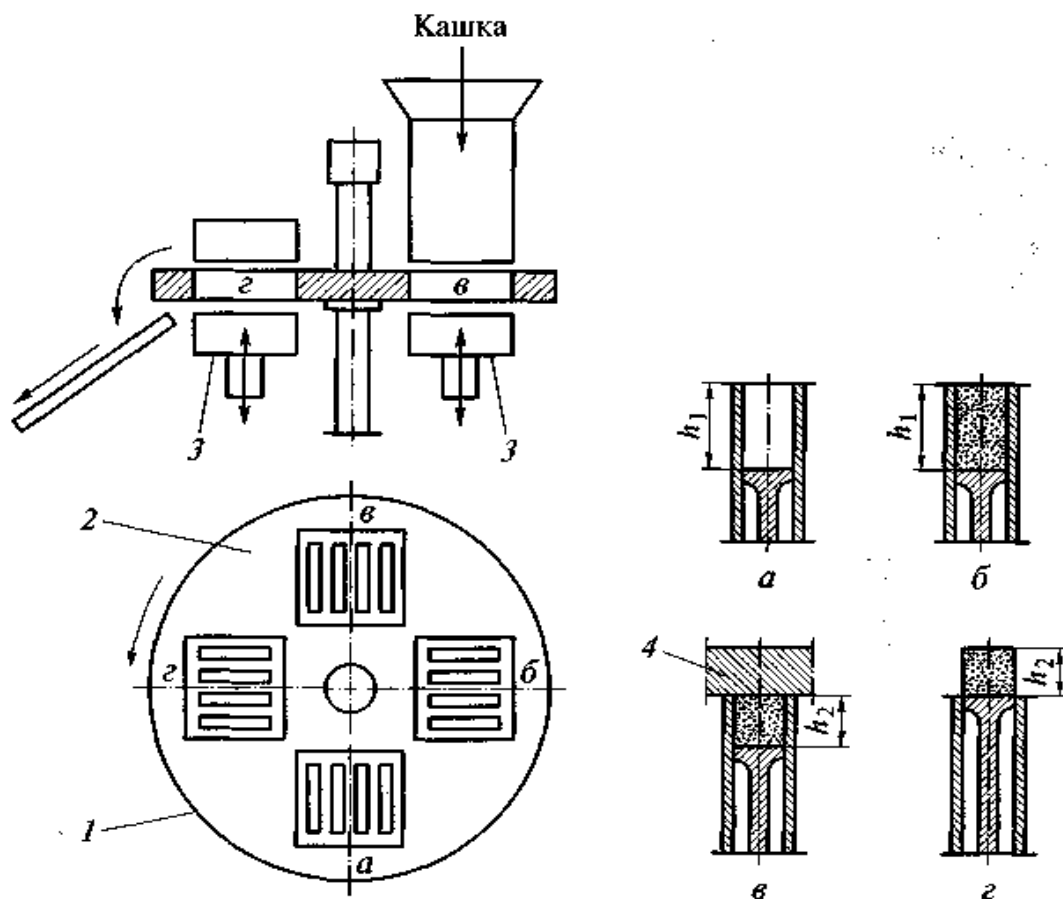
Карусельный пресс с возвратно-поступательным движением пуансона:
